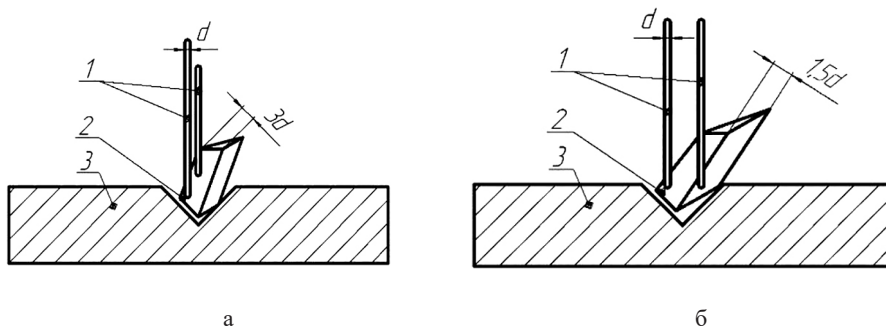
Схема приварки двух электродов к одной (а) и двум (б) плоскостям: 1 – термоэлектрод; 2 – частица порошкового материала; 3 – приспособление для приварки частиц
